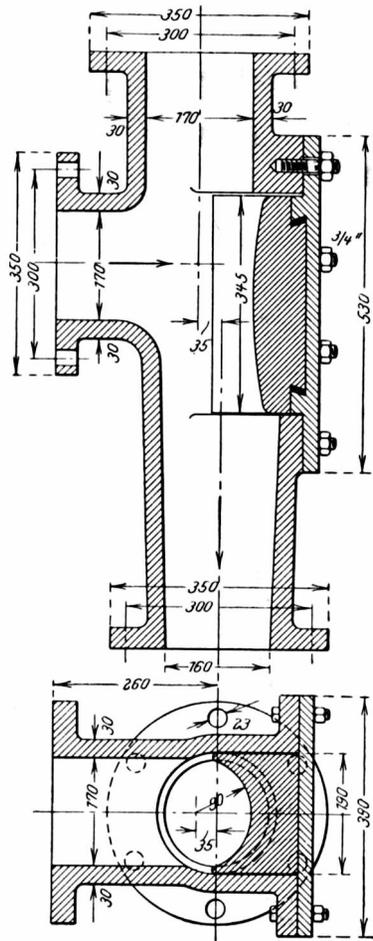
Schachteinlaufkrümmer mit auswechselbarer Verschleißplatte. Friedensgrube.
